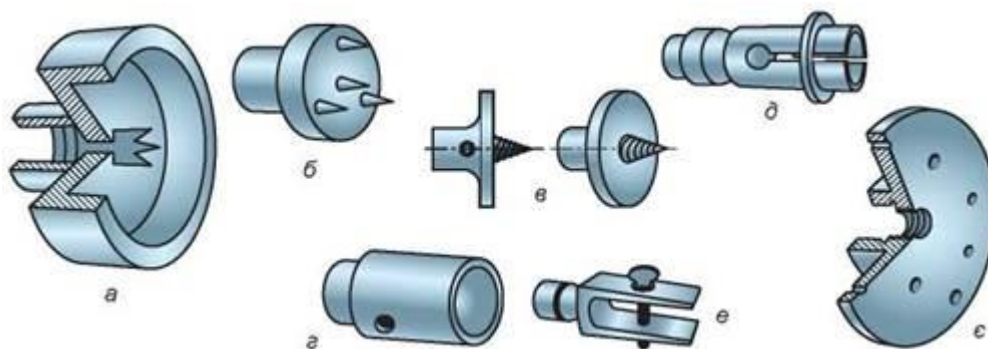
Технологічні пристрої токарного верстата: а - тризуб; б - патрон із шипами; в - патрон з конічним гвинтом; г - чашковий патрон; д - цанговий патрон; е - лещатний патрон; е - планшайба
